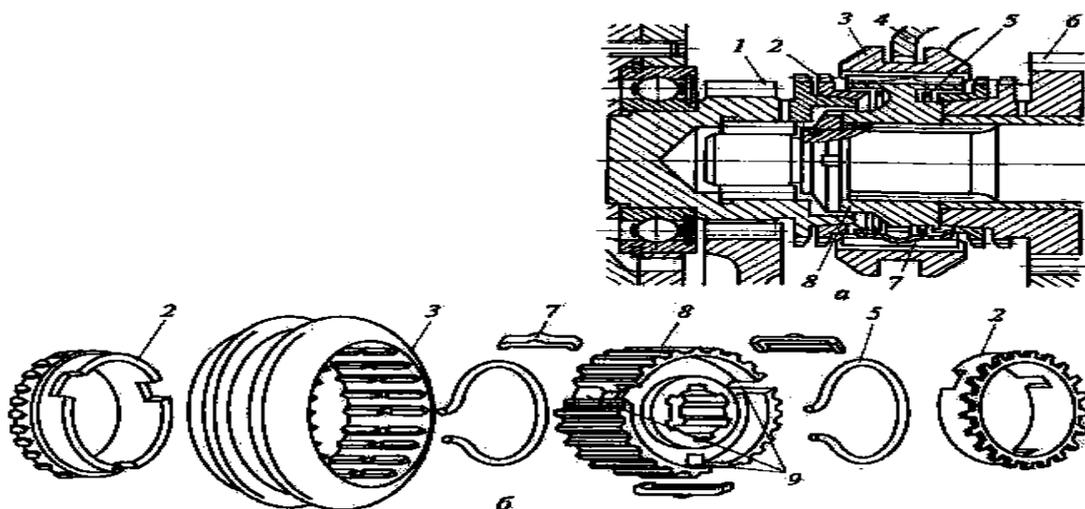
а — конструкция; б — детали; 1 — шестерня ведущего вала; 2 — конусное блокирующее кольцо; 3 — муфта; 4 — вилка; 5 — пружина; 6 — шестерня III передачи; 7 — сухарь; 8 — ступица; 9 — продольные пазы в ступице
